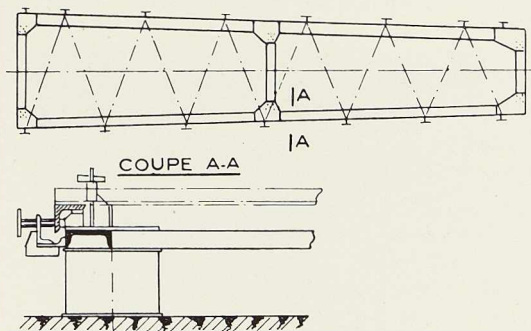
Gabarit de soudage utilisé pour l'assemblage des montants.
